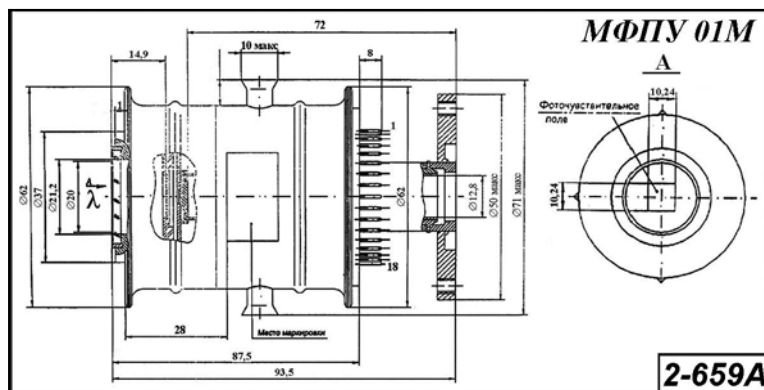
Внешний вид и габаритные размеры модуля МФПУ ОМ1
